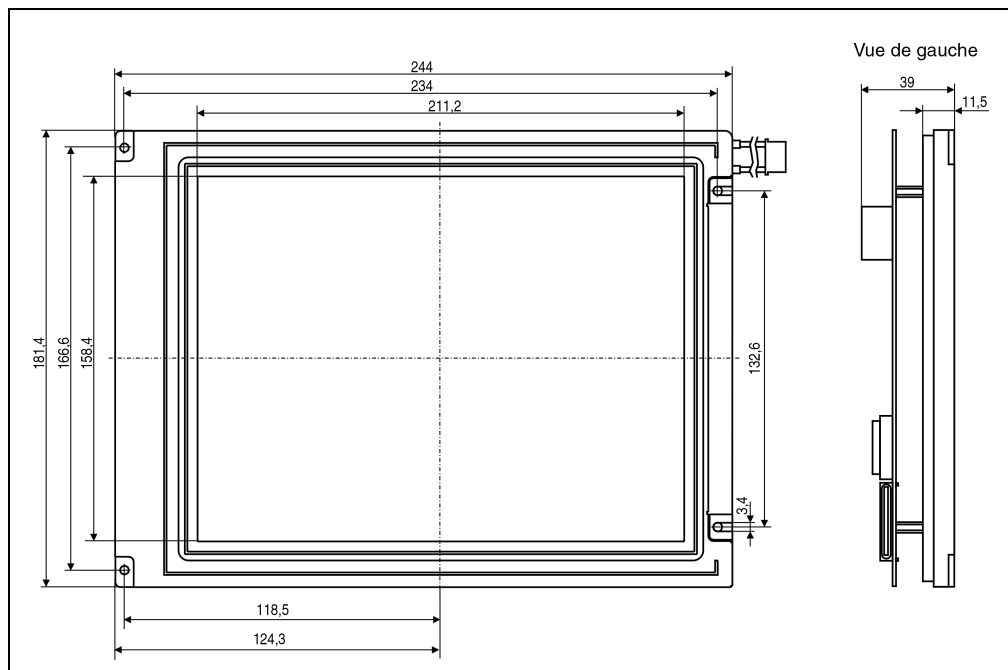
Dimensions du kit écran 5D2000.03 (10,4 pouces)
